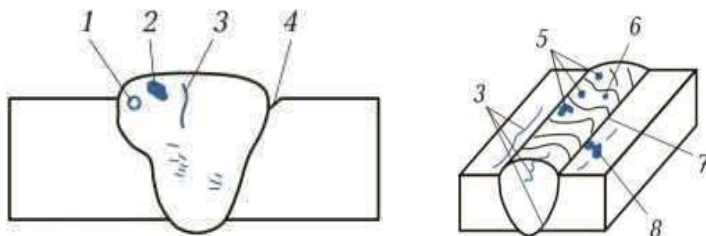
Основные дефекты сварных соединений: 1 — пора; 2 — шлаковое включение; 3 — кристаллизационная трещина; 4 — подрез; 5 — грубочешуйчатая поверхность шва; 6 — поверхностная пора; 7 — цвета побежалости (окисление поверхности); 8 — разбрызгивание.
